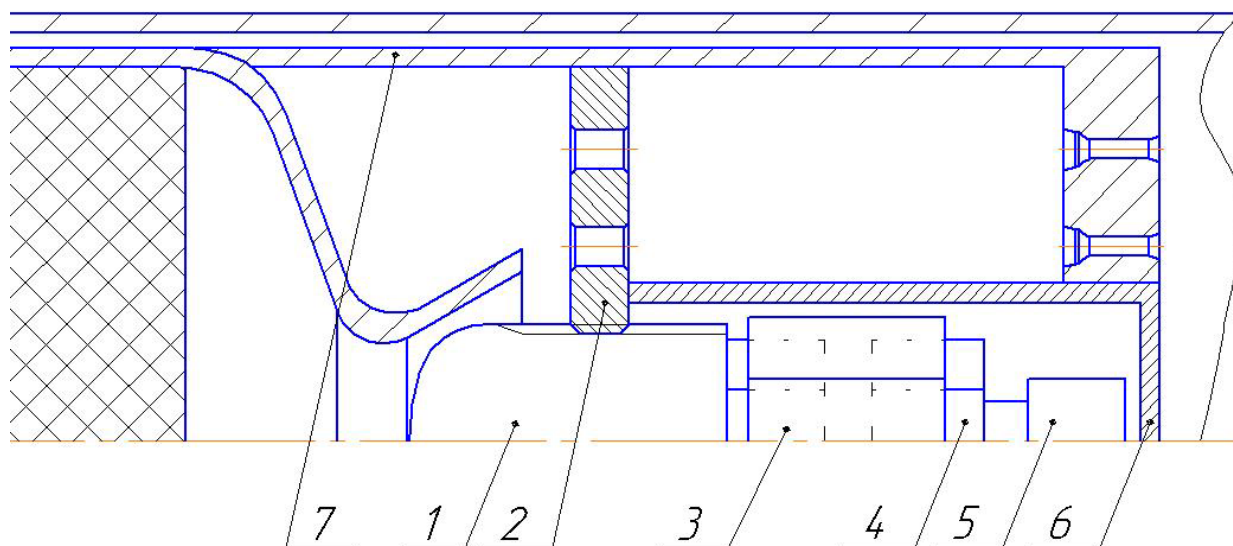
Схема регулирования с помощью передачи винт-гайка
